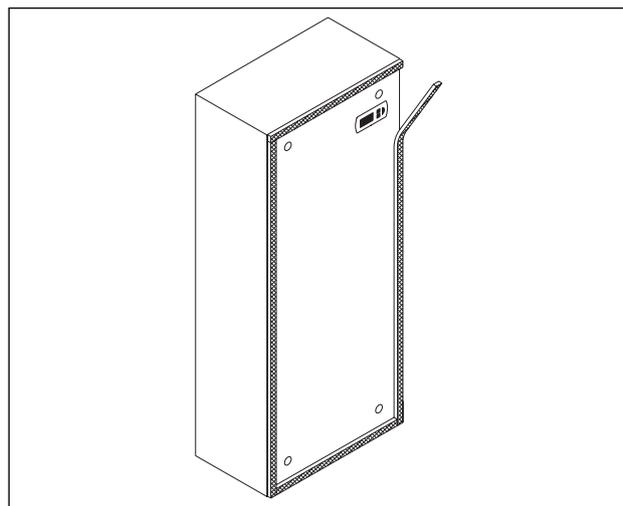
Pose du joint d'étanchéité pour le montage encastré
